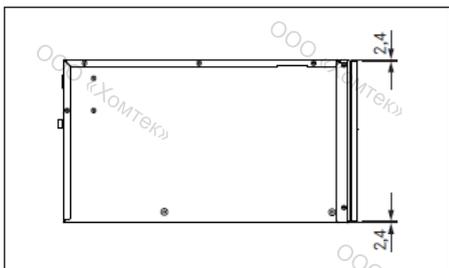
Размеры прибора, модель MS290, вид сбоку
